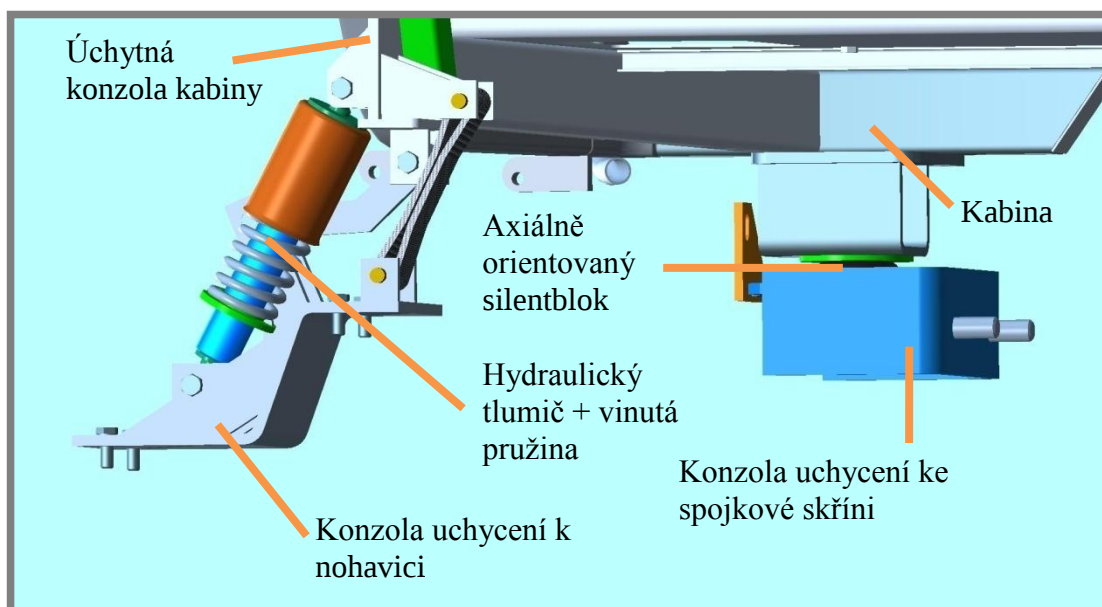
Konstrukční varianta 1, celkový pohled [18]
